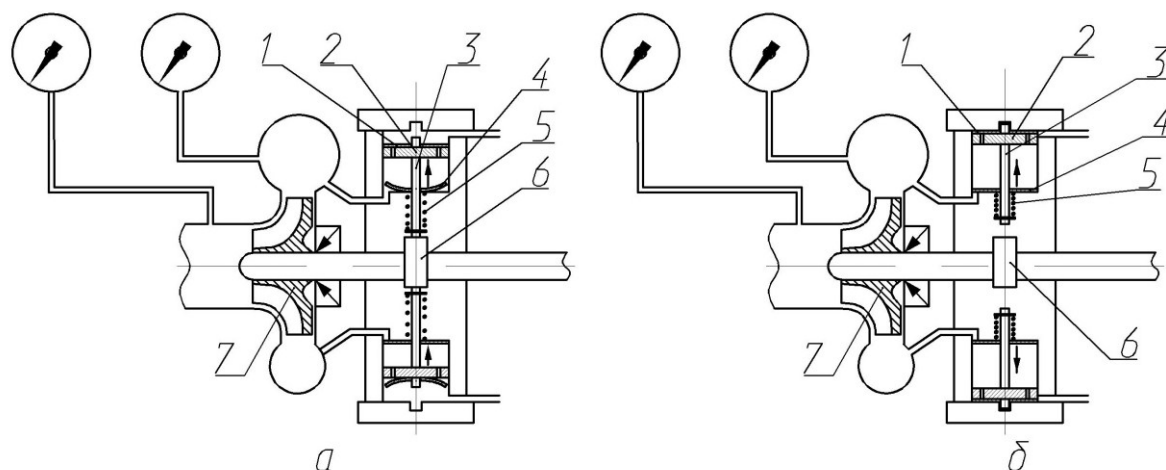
Вакуумная система «ТРОКОМАТ»: 1- нагнетательный клапан; 2- поршень; 3- шток; 4- всасывающий клапан; 5 – возвратная пружина; 6- эксцентрик; 7 – центробежный насос.
